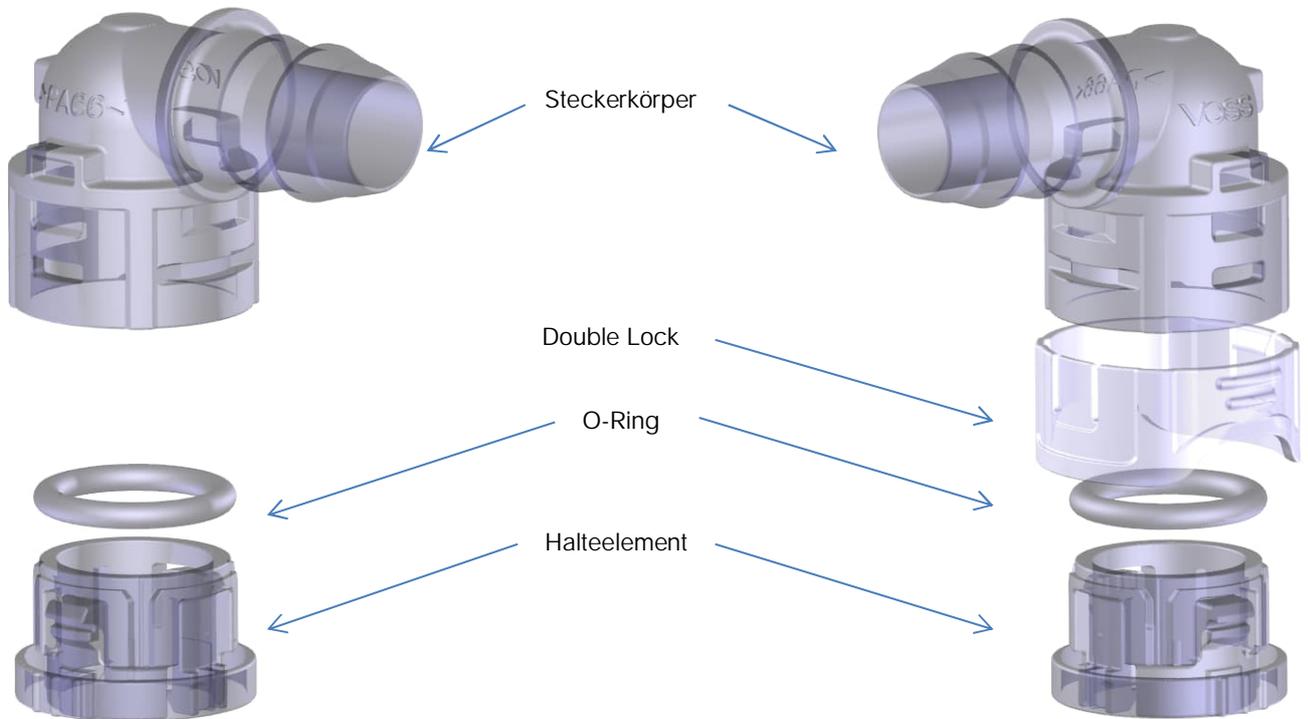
Komponenten der Stecksysteme 270 und 270<sup>DL</sup>
